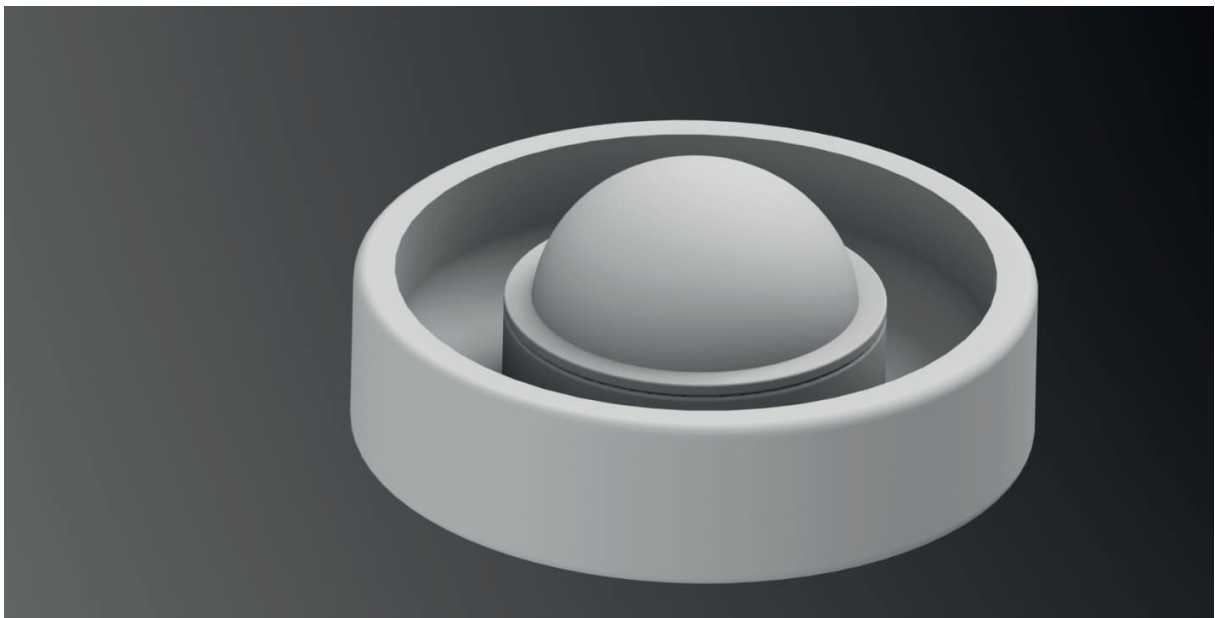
Vista 2 de la solución adoptada del diseño estructural.
